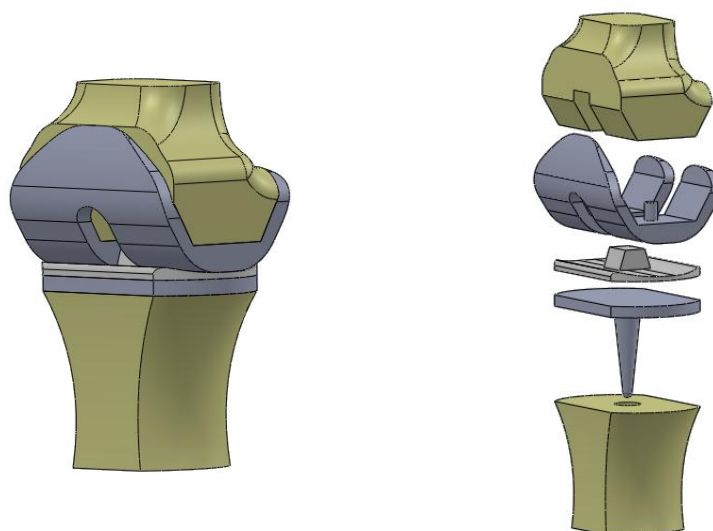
Modelo 3D e vista explodida, utilizando o SolidWorks®.
